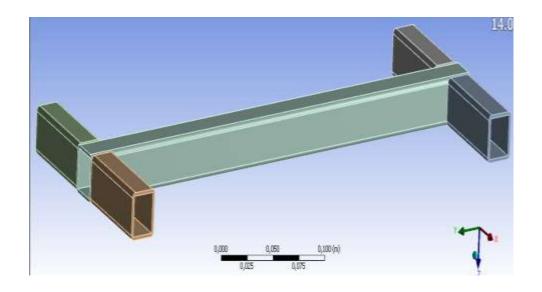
3D модель конструкции под ящик для уплотнителя
